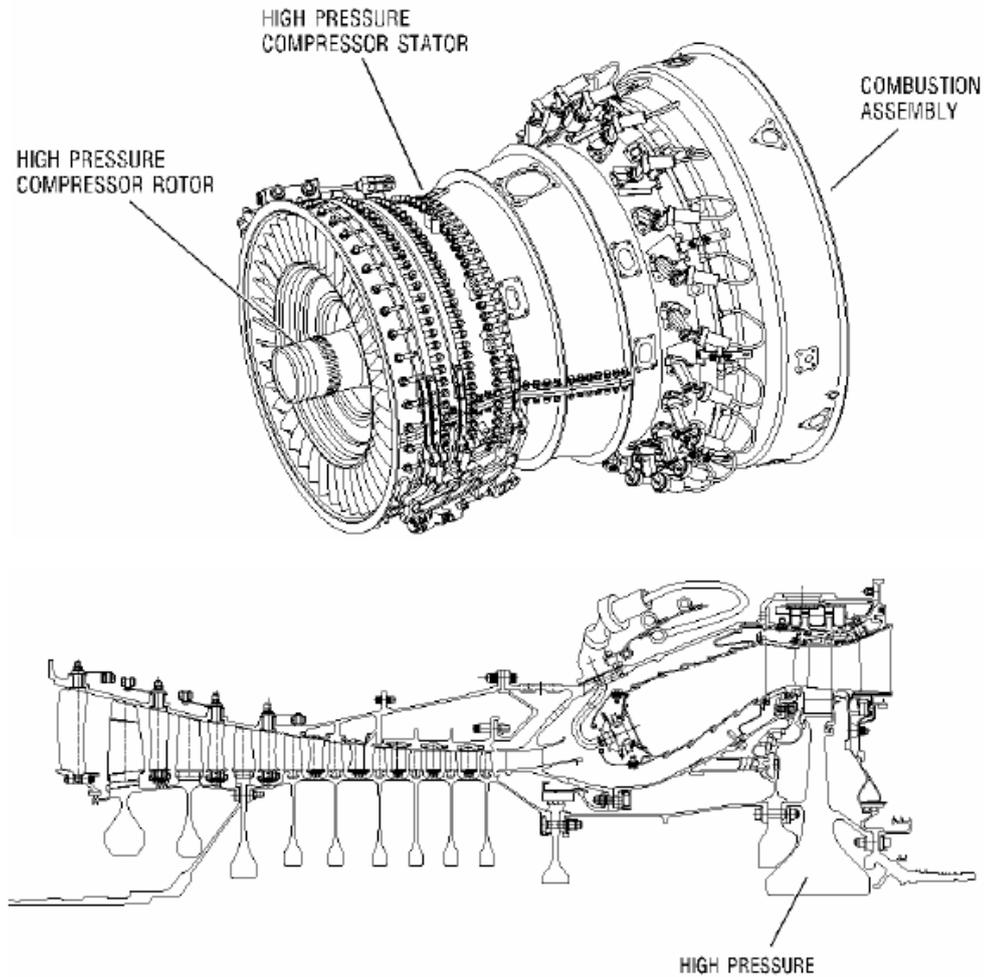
Modulo Mayor Del Compresor De Alta (HPC)
